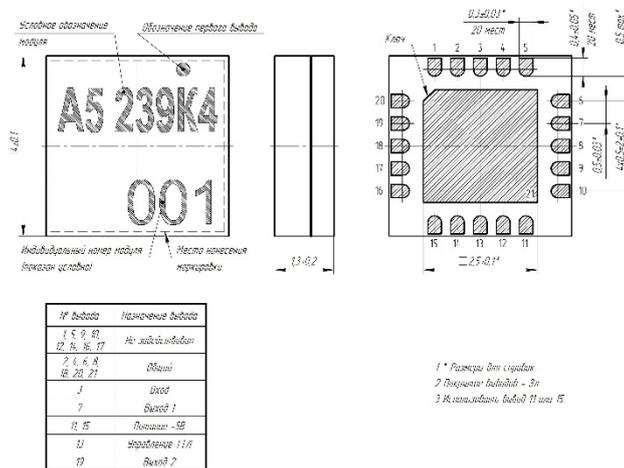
Внешний вид модуля А5.239-К4 (приемка "1"), габаритный чертеж.
